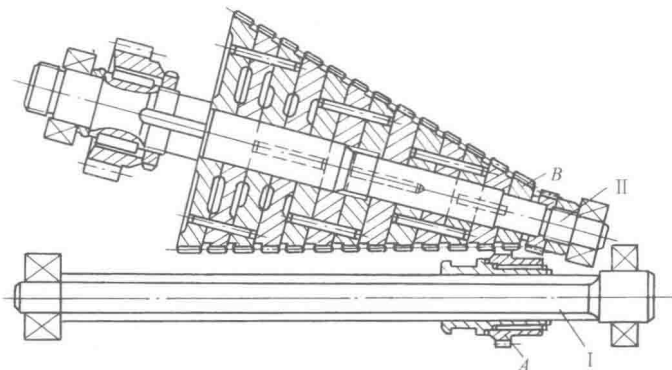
单齿轮滑移锥齿轮组多级变速机构
